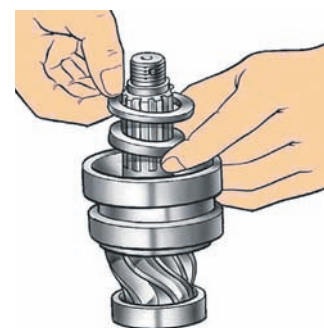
Установку розпірної втулки і регулювальних прокладок переднього підшипника ведучої шестерні
